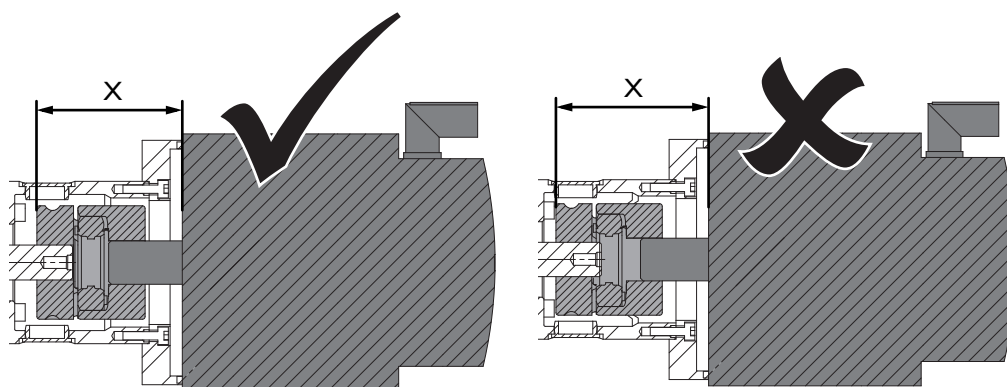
Установить муфту на вал мотора: Использовать допуск "Размер X"
